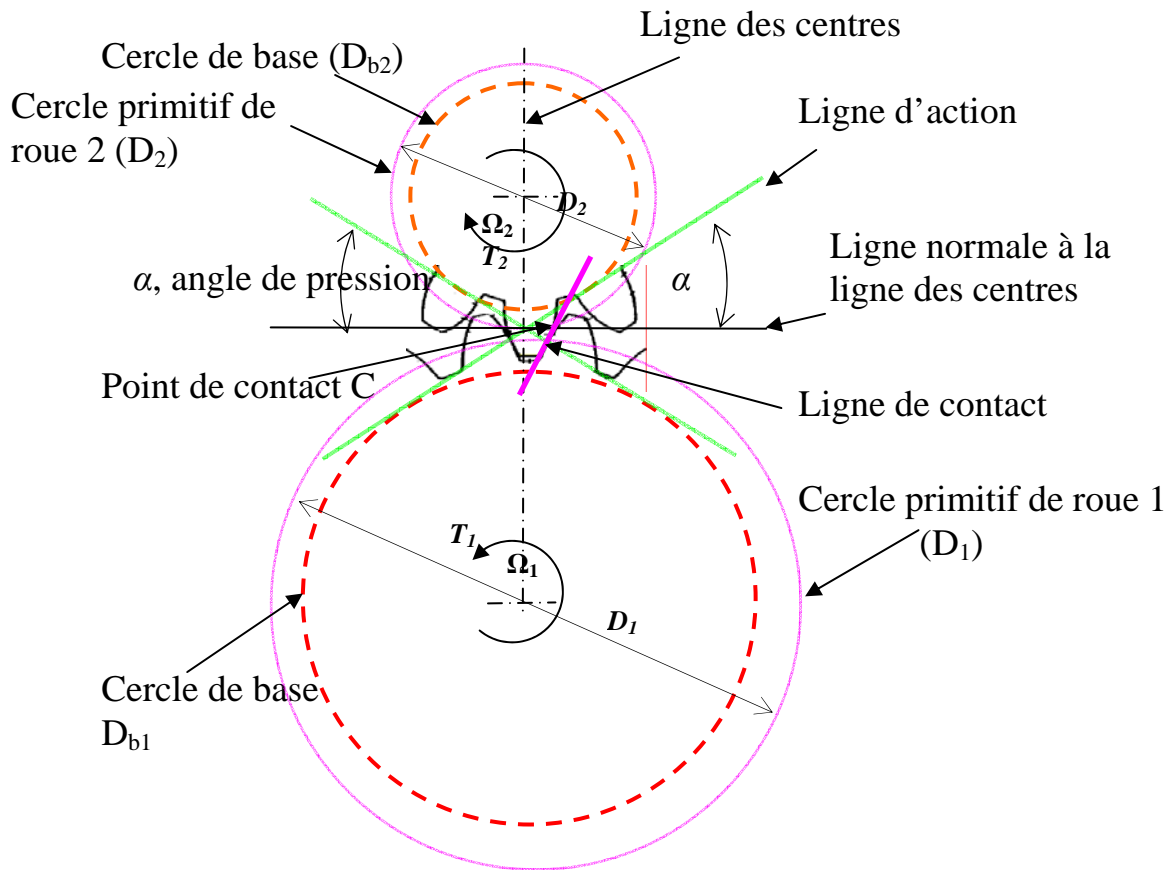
c Géométrie d'un engrenage en contact extérieur
